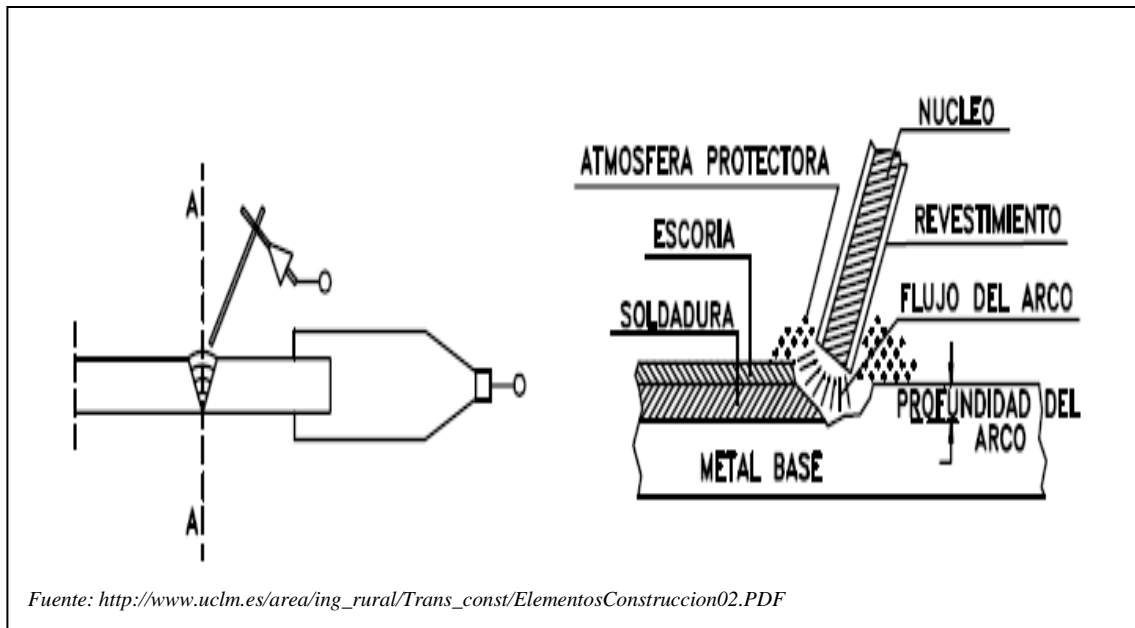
Soldadura Eléctrica con electrodo metálico revestido
